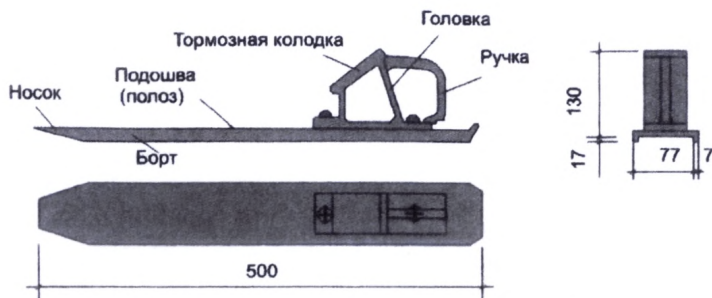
Схематичный рисунок ручного тормозного башмака типа Р-6.
